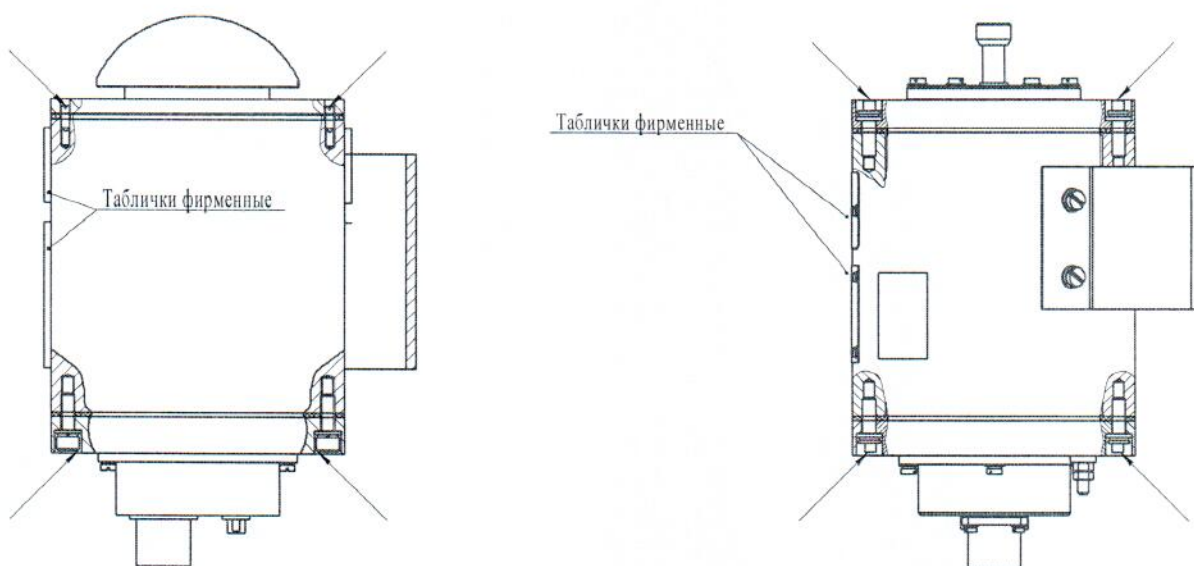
Внешний вид газоанализаторов с принудительным способом отбора пробы исполнения ИБЯЛ.407111.002-02...-49
